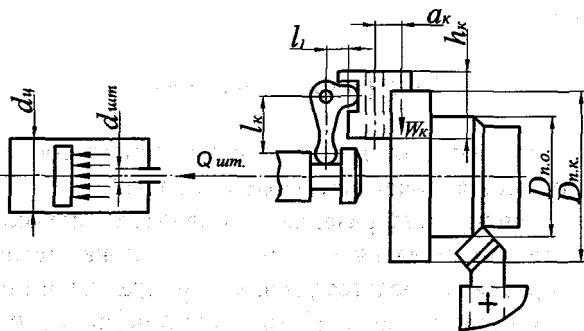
Схема обработки наружного диаметра заготовки при использовании трехкулачкового патрона с пневматическим приводом
